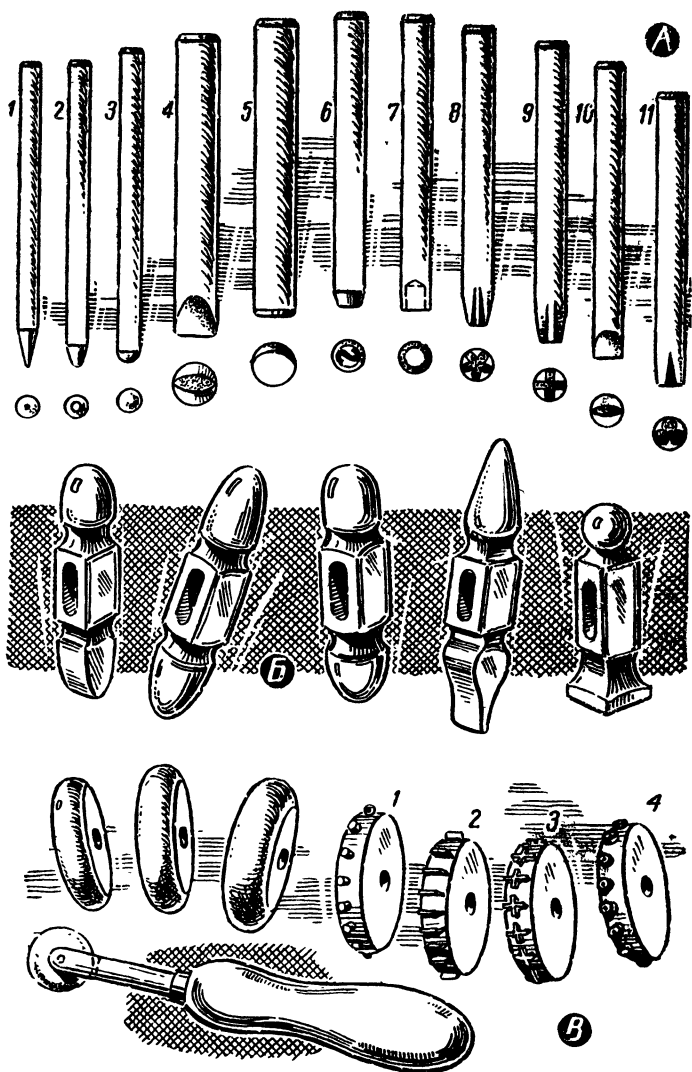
Инструмент для чеканки: А — чеканы; Б — молотки; В — накатки: 1 — накатка для точек; 2 — накатка для черточек; 3 — накатка для крестиков; 4 — накатка для кружков.
